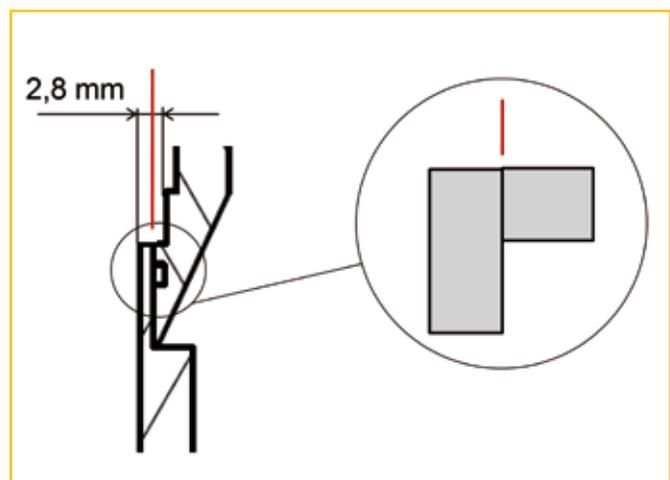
Abweichender I-Stoß nah zum Bauteilrand
